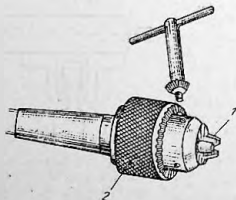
Mandrină pentru fixarea burghiilor cu coadă cilindrică:
